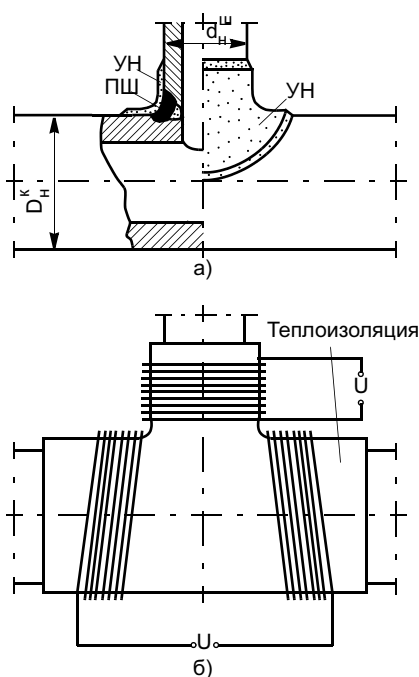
Рекомендуемая схема сварочной технологии ремонта сварного тройника $\varnothing 245 \times 45$ мм/ $\varnothing 159 \times 30$ мм (сталь 15Х1МФ, металл шва 09Х1МФ): а — расположение подварочного шва (ПШ) и усиливающей наплавки воротникового типа (УН); б — размещение нагревательных устройств при проведении высокого отпуска
